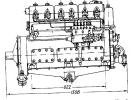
Общий вид двигателя 6 Ч 10,5/13
